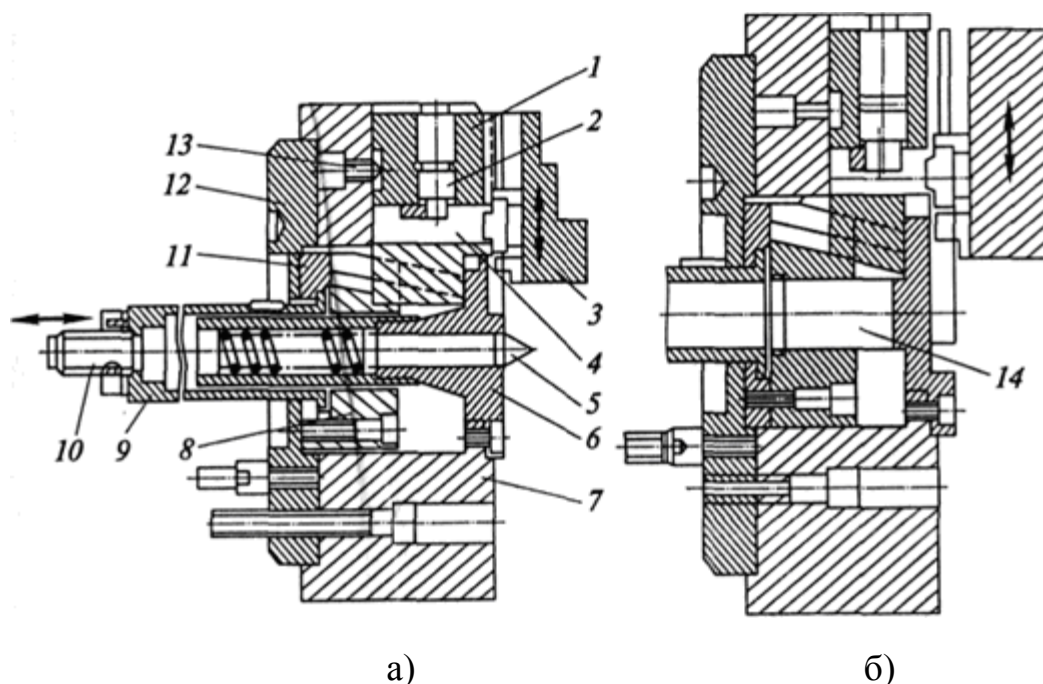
Самоцентрувальний трикулачковий клиновий патрон для обробки заготовок типу вал (а) та диск (б): 1 – основний кулачок; 2 – ексцентрик; 3 – накладний кулачок; 4 – тяга; 5 – плаваючий центр; 6 – змінна вставка; 7 – корпус; 8 – втулка з клиновими замками; 9 – втулка; 10 – гвинт; 11, 12 – фланці; 13 – штифт; 14 – вставка
